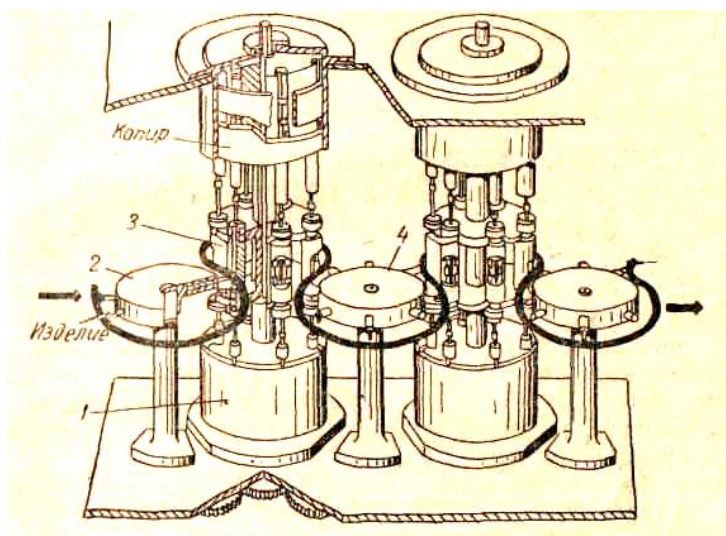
Схема автоматической роторной линии, включающей группу рабочих и транспортных роторов:
